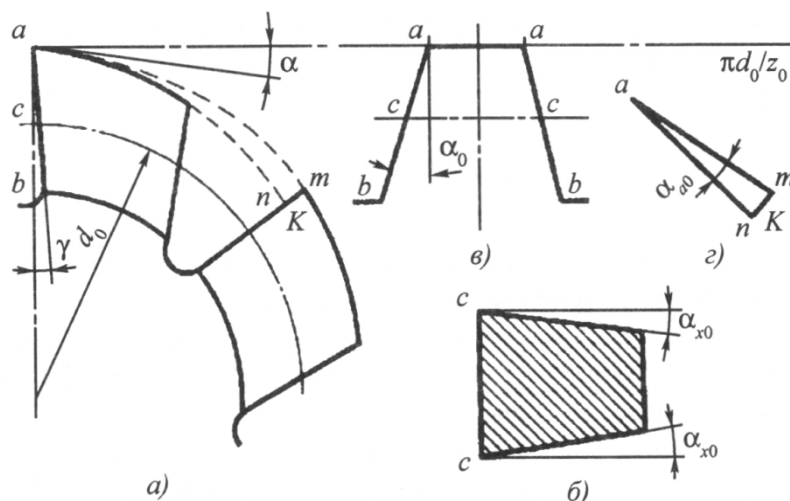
Зубья червячно-модульной фрезы с положительными передними углами и прямолинейными режущими кромками в плоскости передней поверхности зубьев
